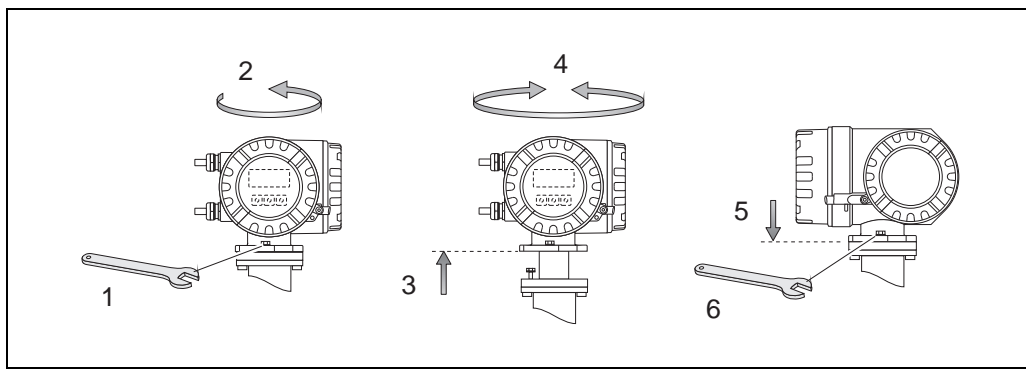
Drehen des Messumformergehäuses (Aluminium-Feldgehäuse)
